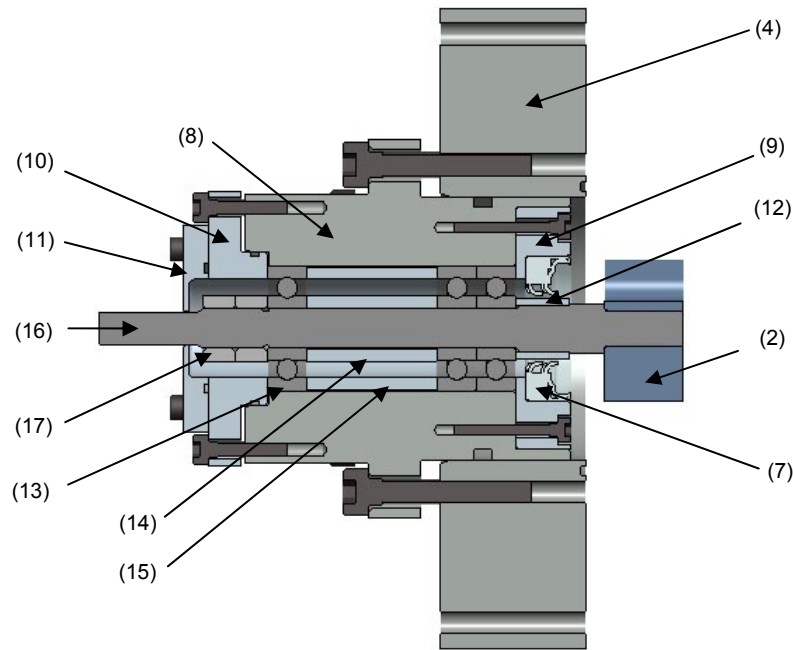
Querschnitt durch die Lagerbaugruppe 626x3
